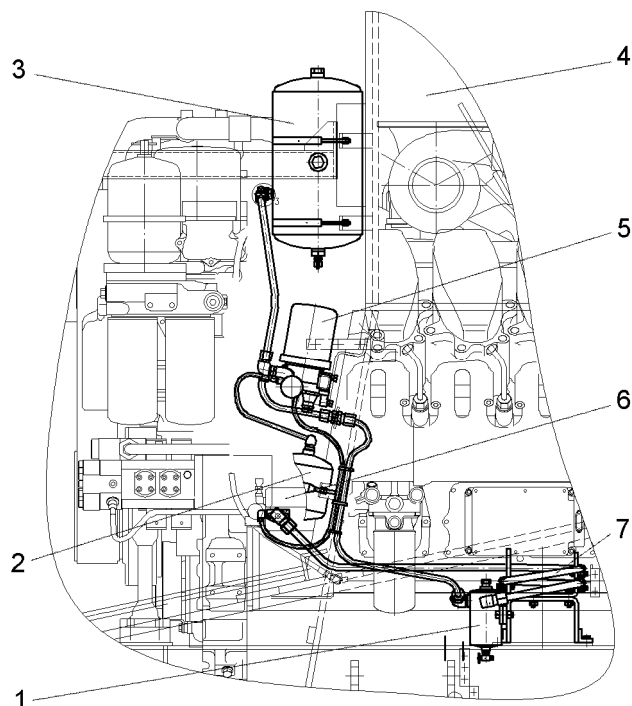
Установка пневматической системы на самосвалах БелАЗ-75302, БелАЗ-75309:
